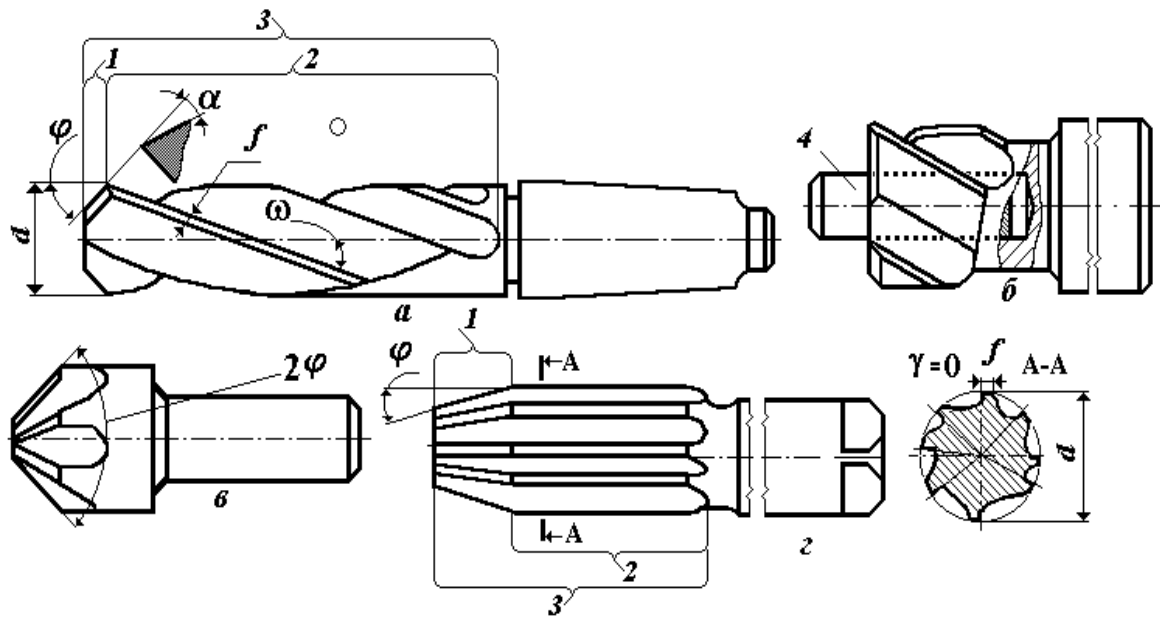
Геометричні параметри різальних інструментів: *а*– зенкер; *б*– цековка; *в*- зенковка; *г*– розвертка; 1 – ріжуча частина; 2– калібрувальна частина; 3– робоча частина; 4– цапфа; *d*– істинний діаметр розвертки; *f*– ширина стрічки; α , γ , φ , ω - кути різання.
